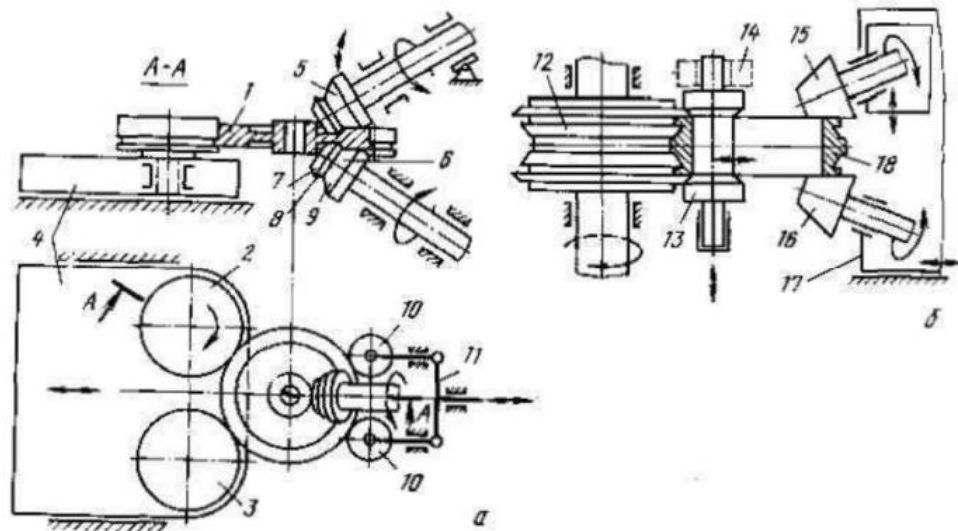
Схеми прокатки на колесопрокатному (а) і кільцепрокатному (б) станах: 1 - прокатуване колесо; 2, 3 - приводний і не приводний корінні валки; 4 - каретка переміщення корінних валків; 5, 6 - похилі праведні валки (верхній - регульований, нижній - стаціонарний у вертикальному напрямку); 7, 8, 9 - кінцевий, середній і початковий конуси похилих валків; 10 - натискні не приводні валки, регульовані в горизонтальному напрямку; 11- система регулювання положення натискних валків, що забезпечує вирівнювання зусиль на них; 12 – приводний стаціонарний валок (головний); 13 - внутрішній не приводний валок (дорн), регульований у горизонтальному напрямку (опускаємий при задачі в стан заготовки кільця); 14 - накидна додаткова опора; 15, 16 - приводні похилі валки (верхній - регульований, нижній - стаціонарний у вертикальному напрямку); 17 - каретка горизонтального переміщення похилих валків; 18 - прокатуване кільце
